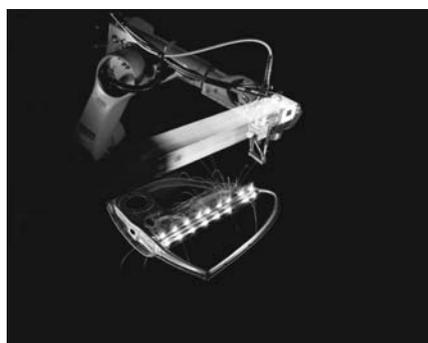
Welding-on-the-fly mit dem Festkörperlaser
